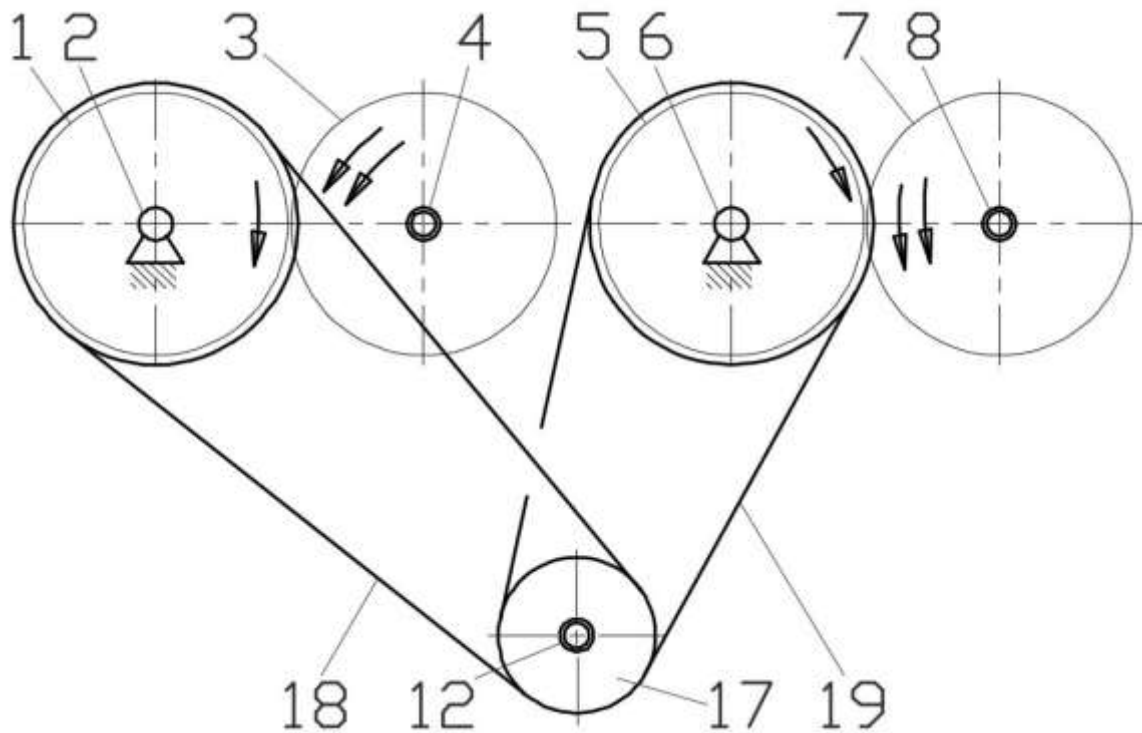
Привід вальцьового верстата від трансмісійного вала.
